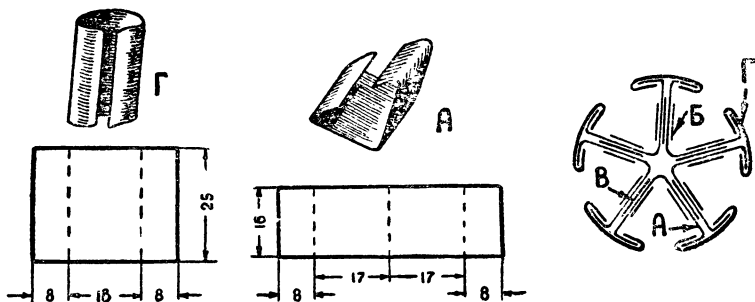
Основные детали и конструкция пятиполюсного якоря.
